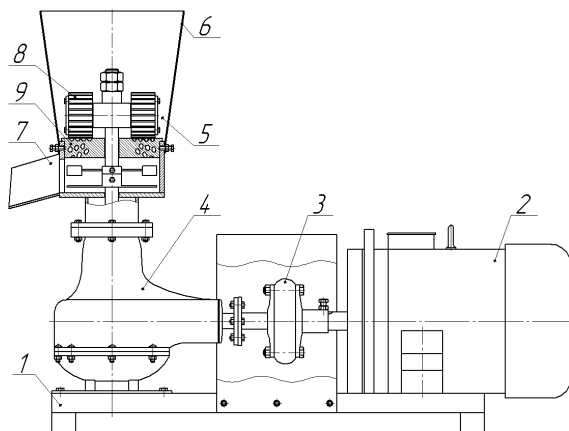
Конструктивно-технологічна схема робочих органів гранулятора з нерухомою матрицею та рухомими прикочувальними роликami: 1 – рама; 2 – електродвигун; 3 – запобіжна муфта; 4 – редуктор; 5 – корпус; 6 – завантажувальна горловина; 7 – вивантажувальний патрубок; 8 – прикочувальні ролики; 9 – матриця
